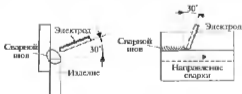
Положение электрода при сварке нахлесточного соединения в горизонтальном положении
